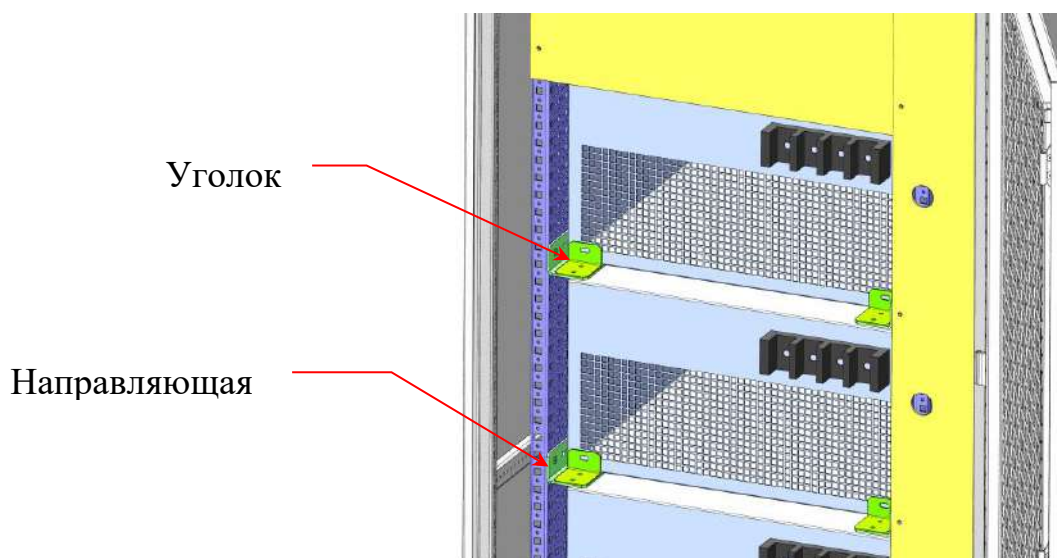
Схема крепления силового модуля RU-DRIVE DVR внутреннего исполнения
